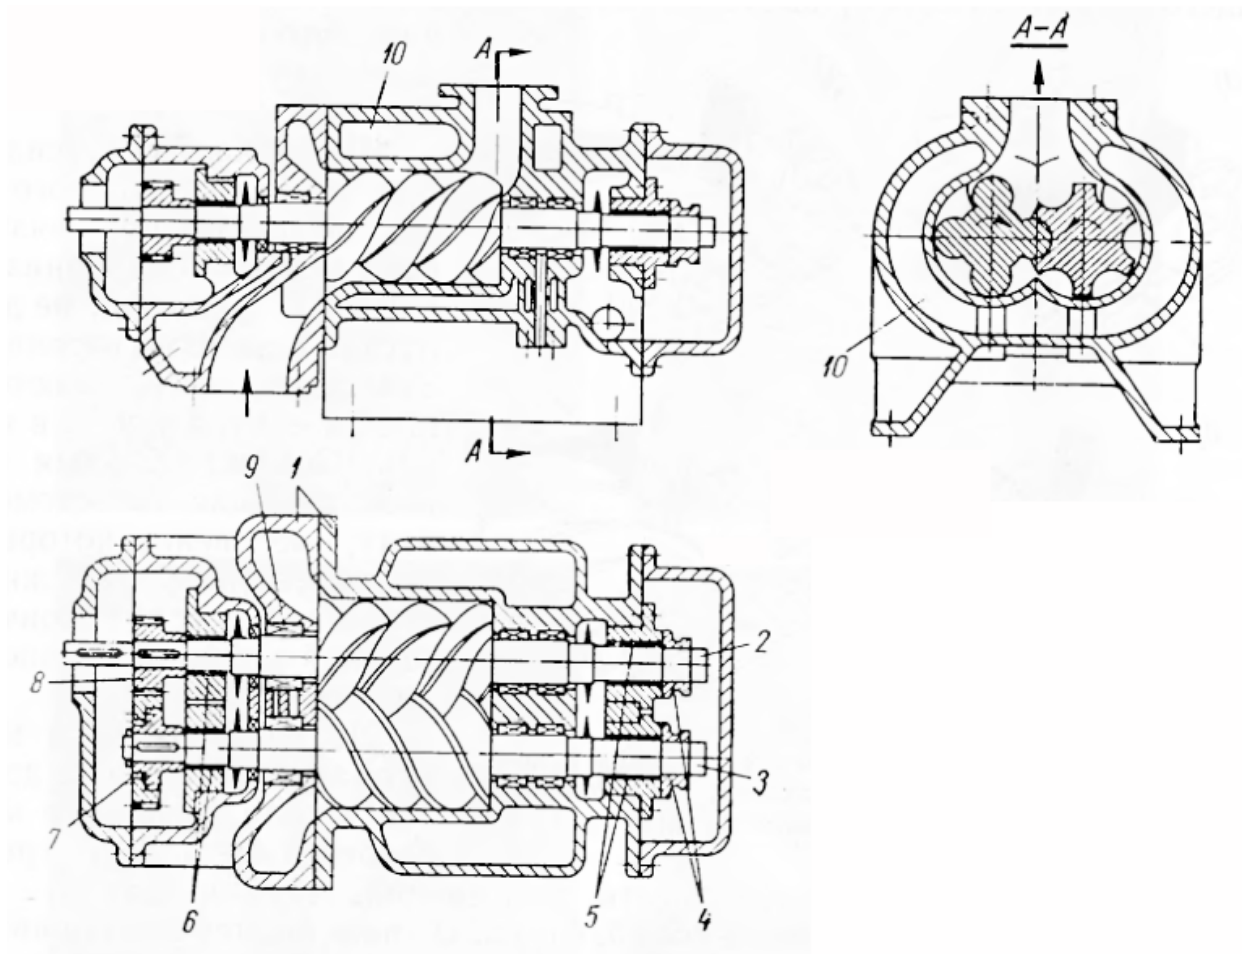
Конструктивна схема гвинтового компресора
